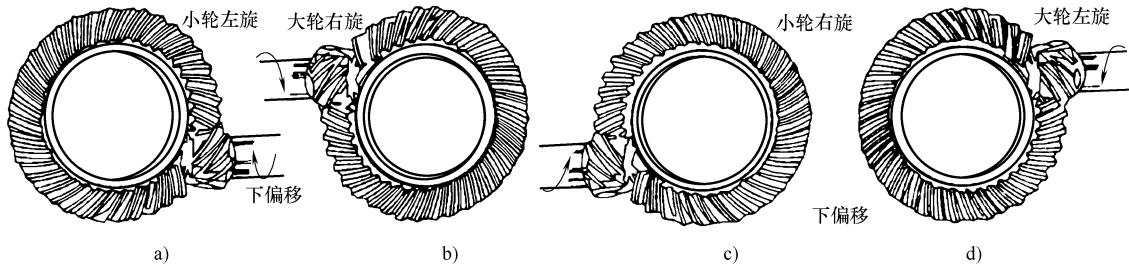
准双曲面锥齿轮的偏移与螺旋方向
